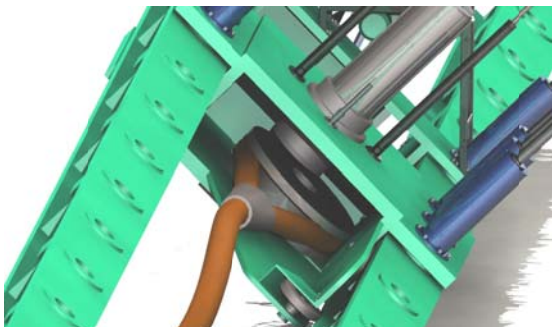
Conjunto cabo mais ferramenta já dentro da gaveta
